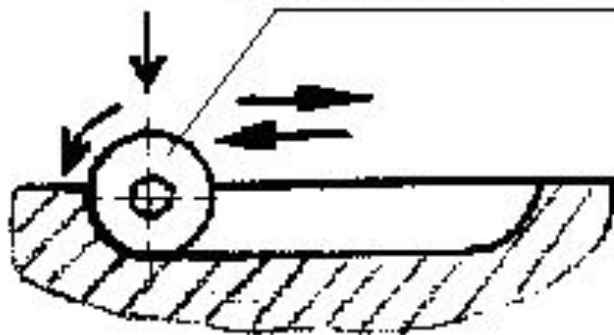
Нарезание шпоночного паза дисковой трехсторонней фрезой
